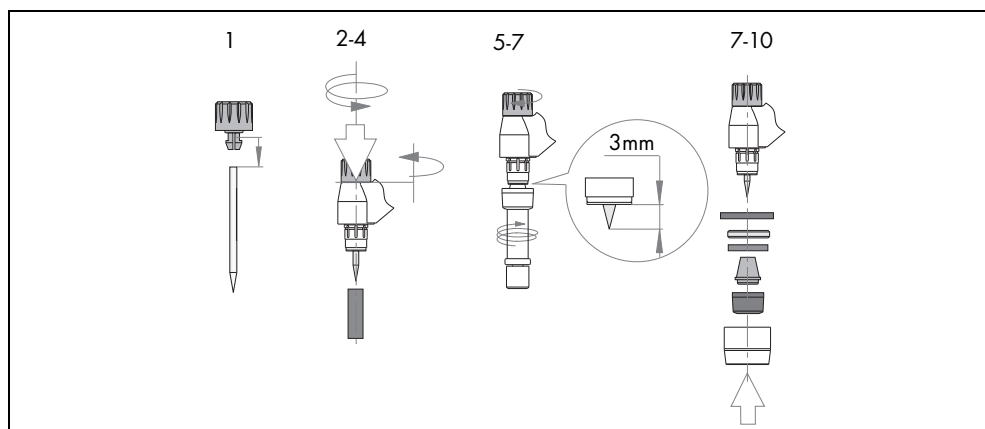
Pasos para equipar el cuerpo de antorcha ABIPLAS® WELD 250 MT
